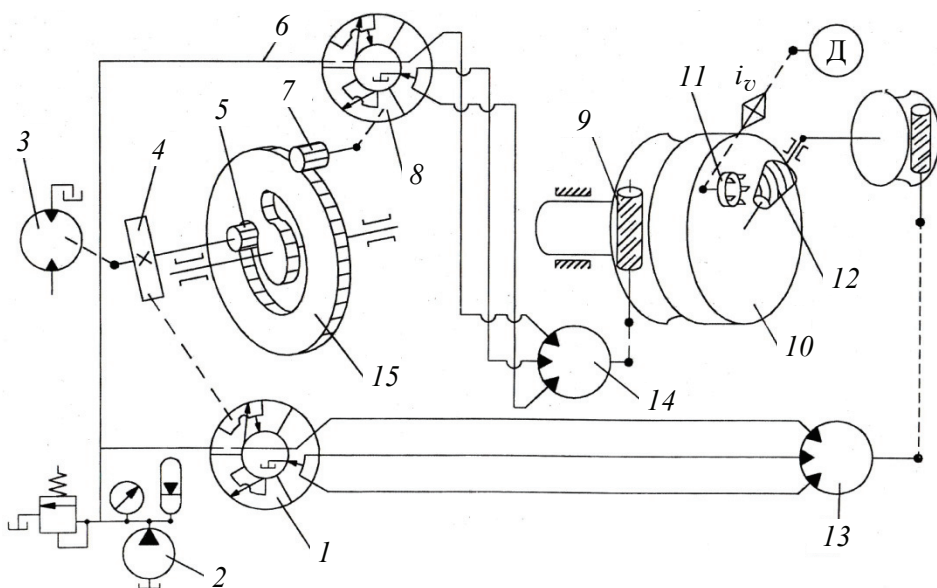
Структурная схема зуборезного станка с гидравлическими связями во внутренней цепи для нарезания конических колес с криволинейным зубом резцовой головкой
